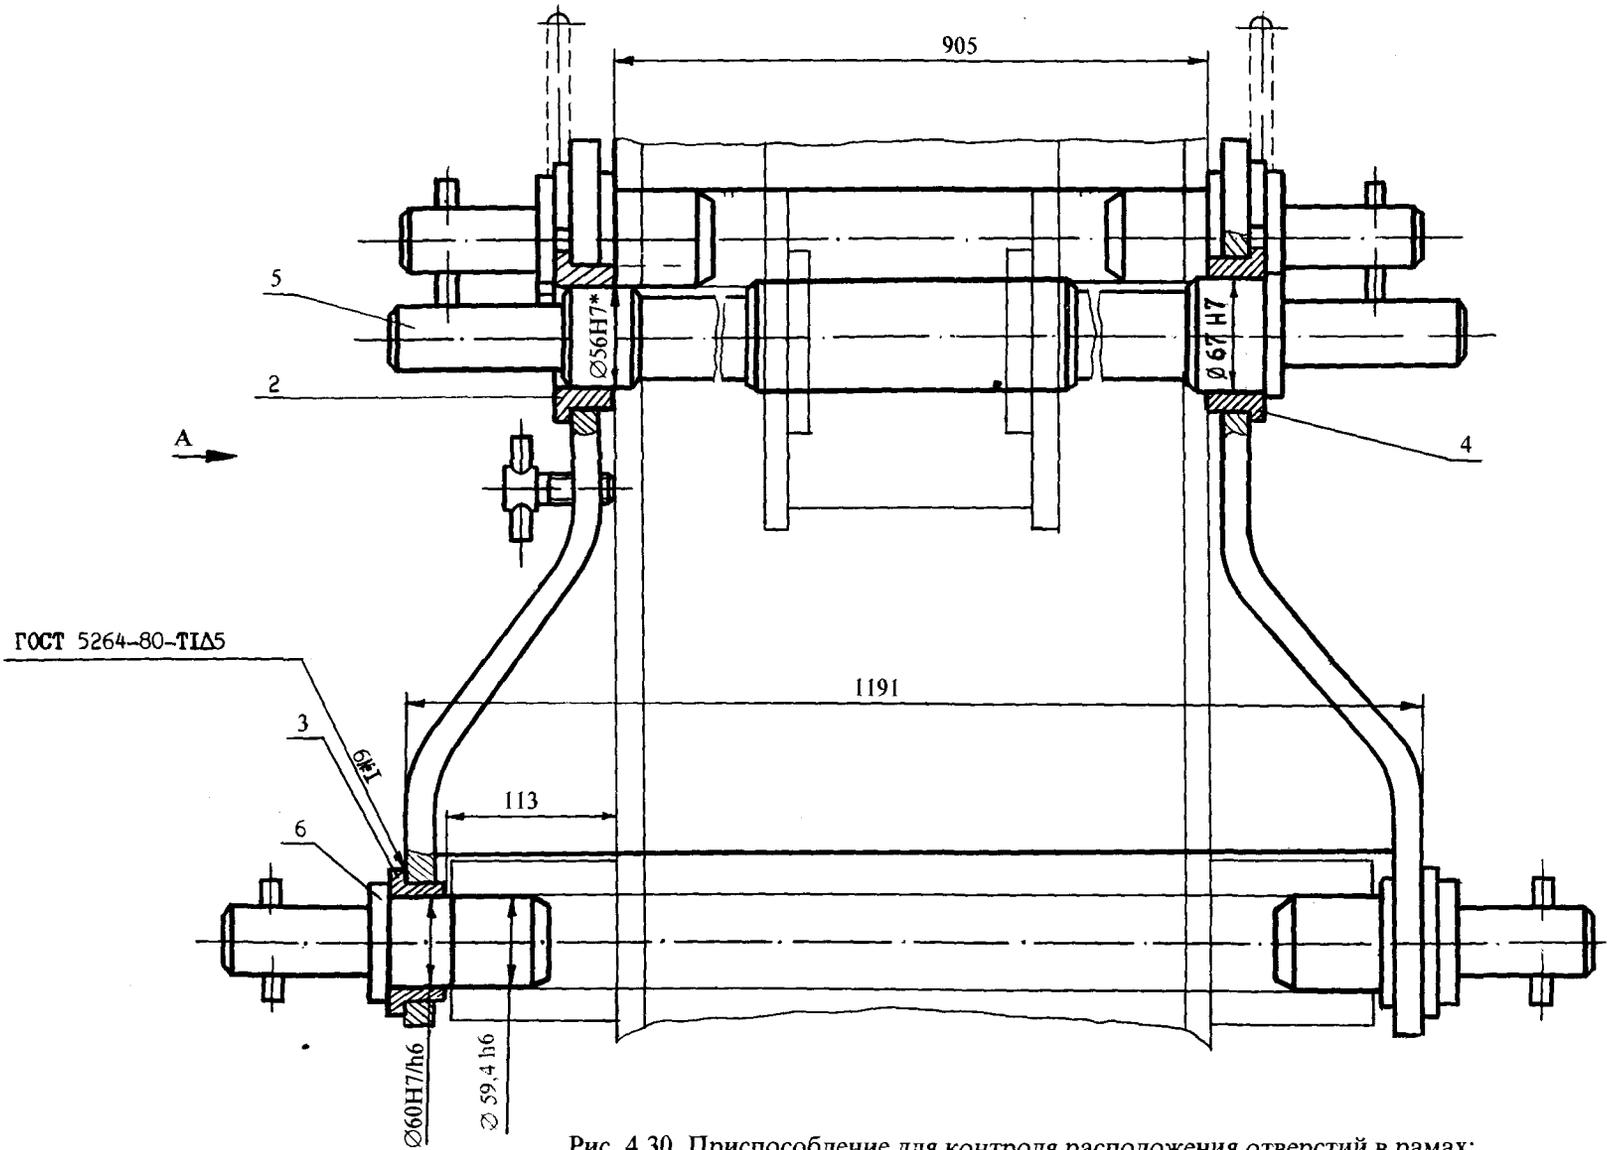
Приспособление для контроля расположения отверстий в рамах:
